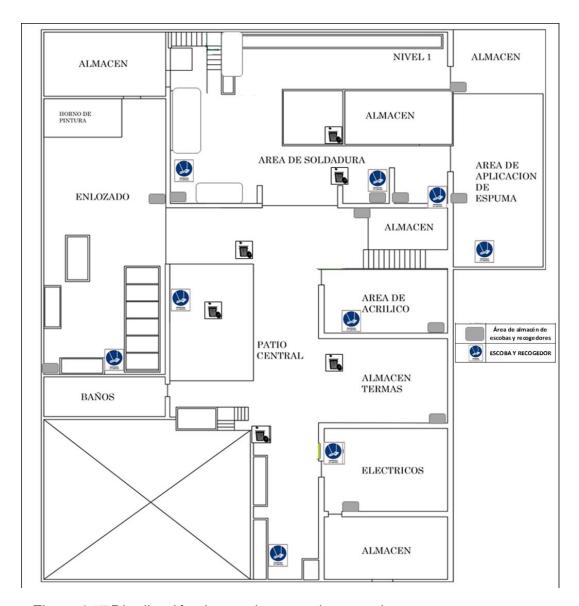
Distribución de escobas y tachos en planta Elaborado por: los autores
